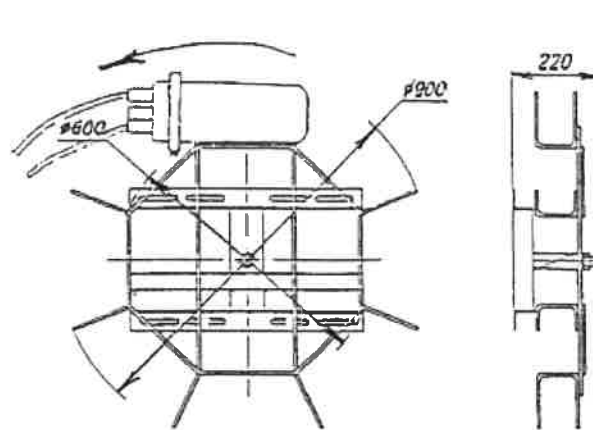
Устройство для намотки подвесного ОК и схема закрепления муфты
